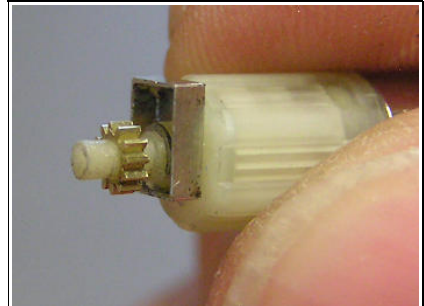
Den Motorhalter aufstecken und das Zahnrad Z12 auf die Motorwelle stecken. Die endgültige Position wird mit dem Getriebegehäuse eingestellt.
